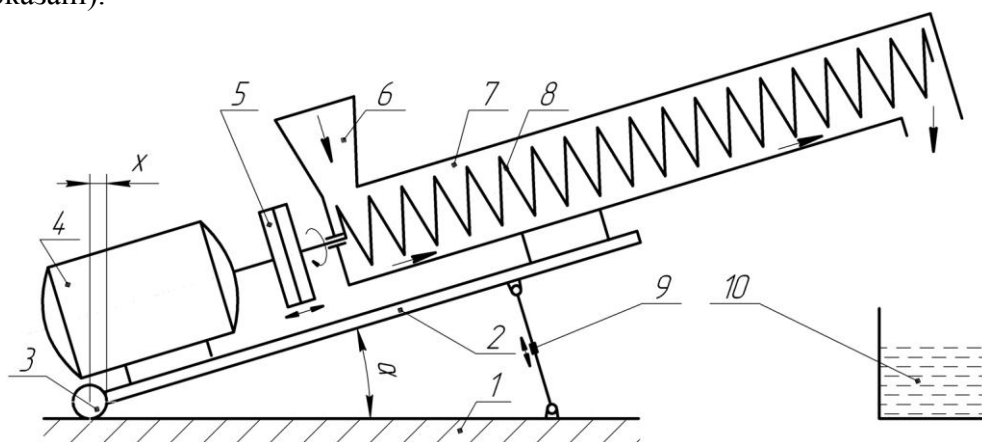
Принципова схема компонування приводу не горизонтальних транспортно-технологічних систем: 1 – рама; 2 – плита; 3 – поворотний шарнір; 4 – електродвигун; 5 – запобіжна муфта; 6 – бункер; 7 – кожух; 8 – гвинтовий робочий орган; 9 – гвинтова регульовальна пара; 10 – смінь.
